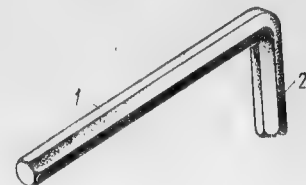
1 — рукоятка; 2 — рабочая часть
